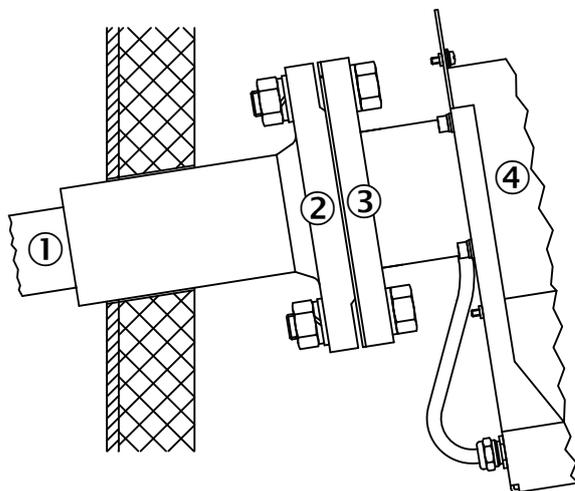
Montage du tube de prélèvement sur la bride à souder
